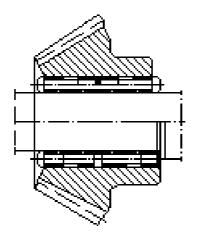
Fixação de engrenagem cônica com bucha HBK
